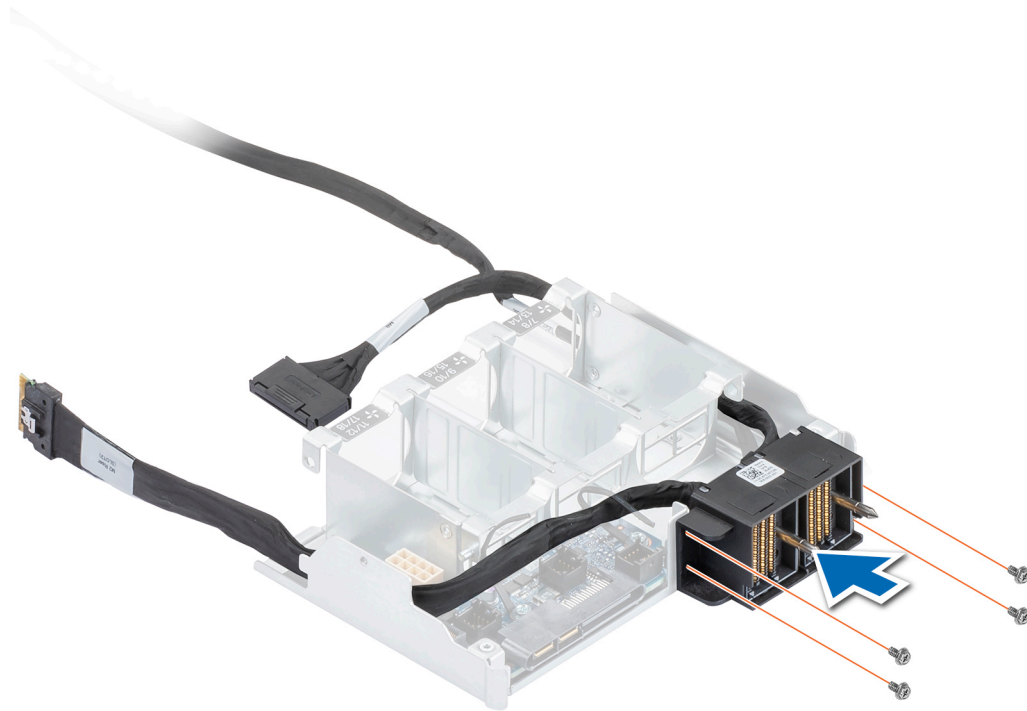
Entfernen des Schlitten-Kabel-Kits
